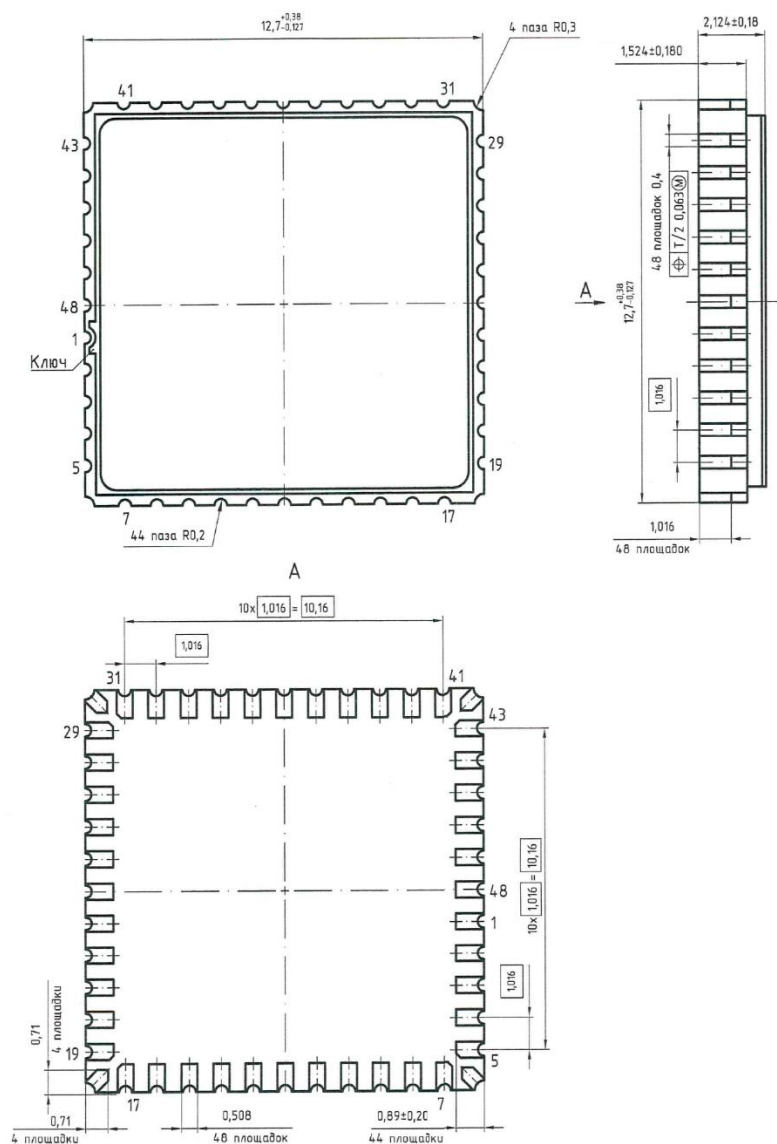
Габаритный чертёж корпуса 5142.48-A (размеры в мм)
